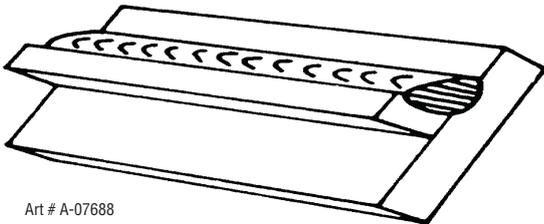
Position à plat, soudure d'angle par gravité
